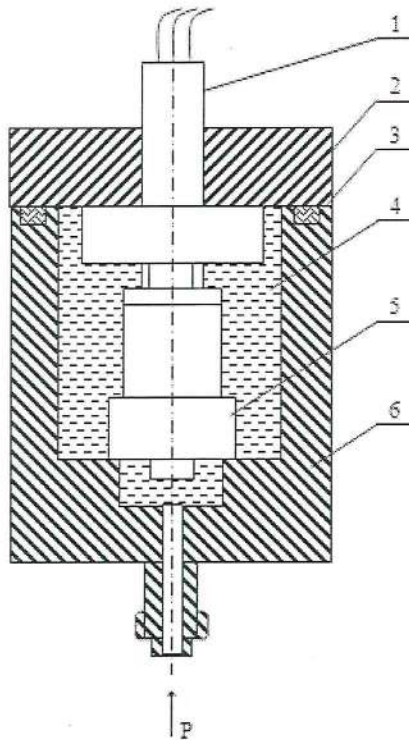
Схема приспособления для испытания тензопреобразователя гидростатическим давлением
